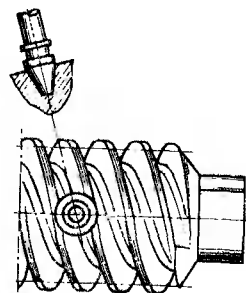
Цилиндрический, образованный конусом червяк ZK3
